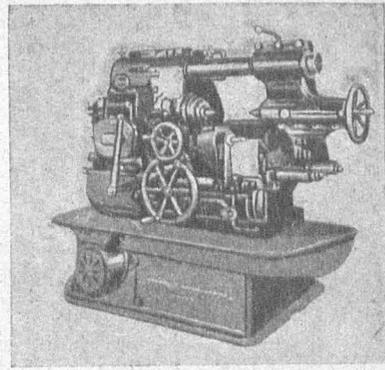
Многорезцовый токарный станок МТ-30. Максимальный диаметр обрабатываемого предмета 350 мм. Число скоростей шпинделя 12
